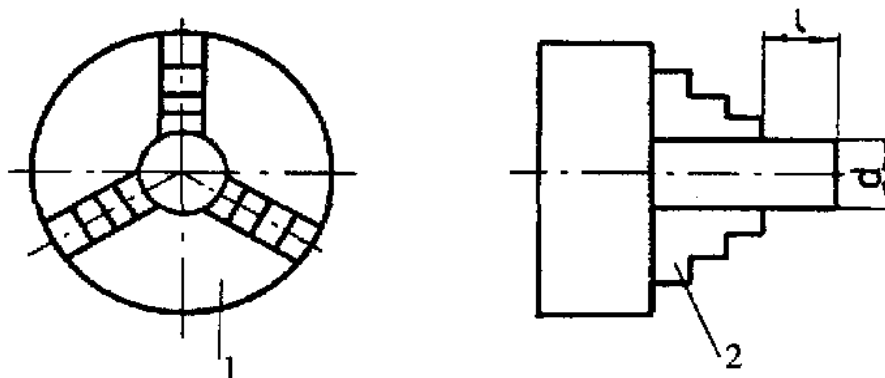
Схема установки заготовки в трехкулачковом патроне
